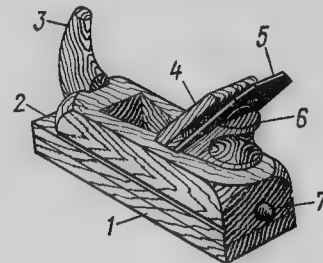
1 — нижняя часть колодки (подошва); 2 — верхняя часть колодки (корпус); 3 — рог; 4 — клин; 5 — нож со стружколомом; 6 — упор; 7 — пробка
